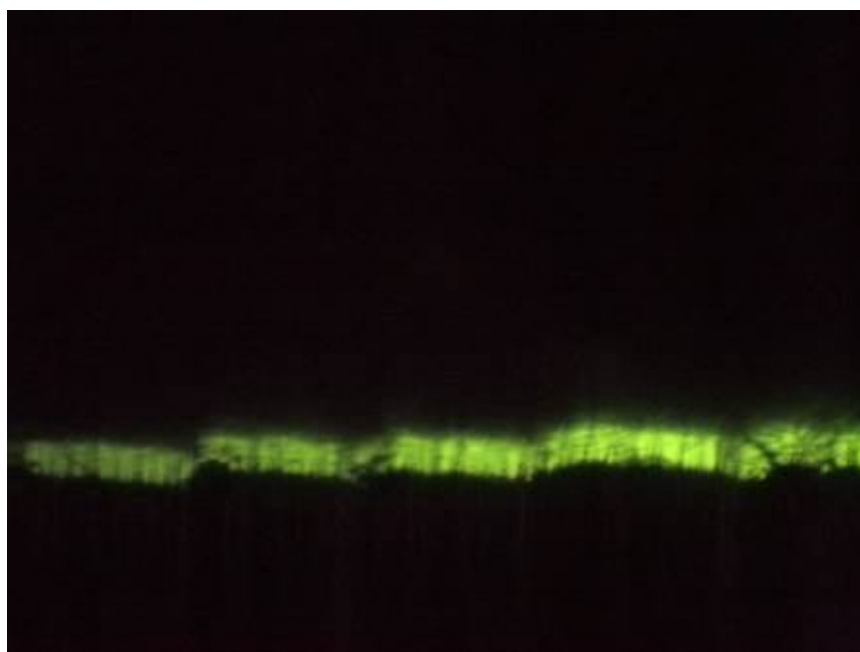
Шероховатость поверхности стали с применением СОЖ – ТМ-2 при черновой обработке.
